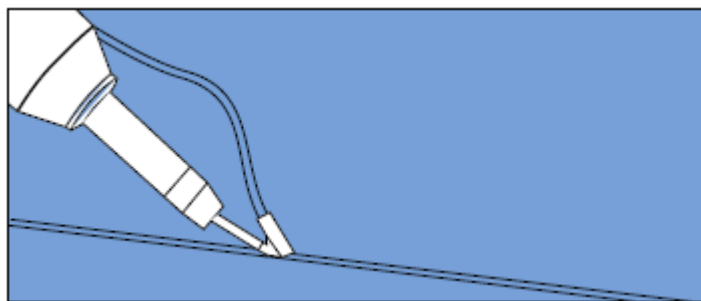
Aplicação do cordão de soldar com pistola de ar quente [11]
